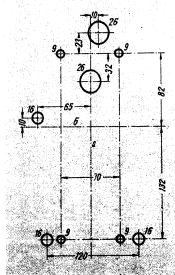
Сверление отверстий для установки на изоляционных плитах контакторов типа КП 504 и КП 514 с задним присоединением
